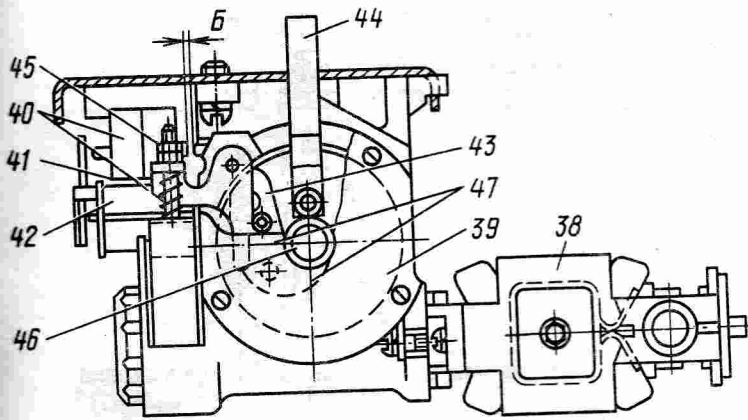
Электродвигательный привод с блоком управления выключателя Э06
